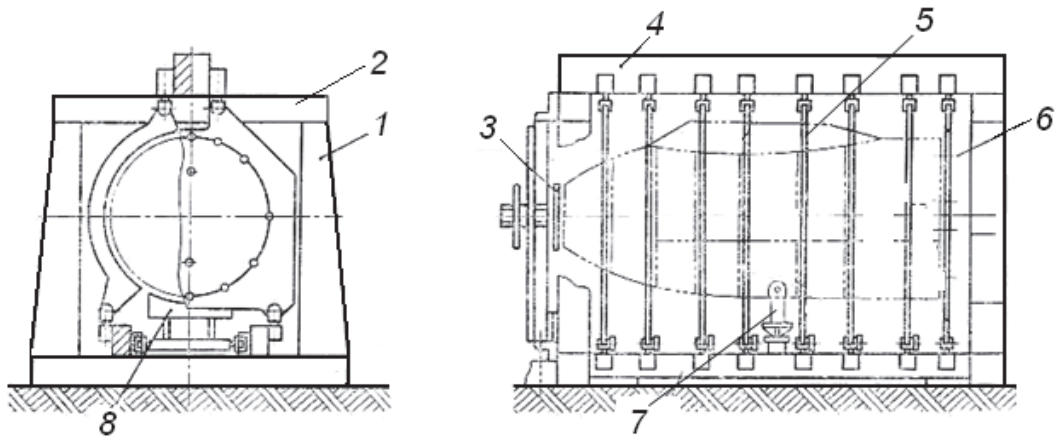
Конструктивная схема стапеля сборки НОФ
